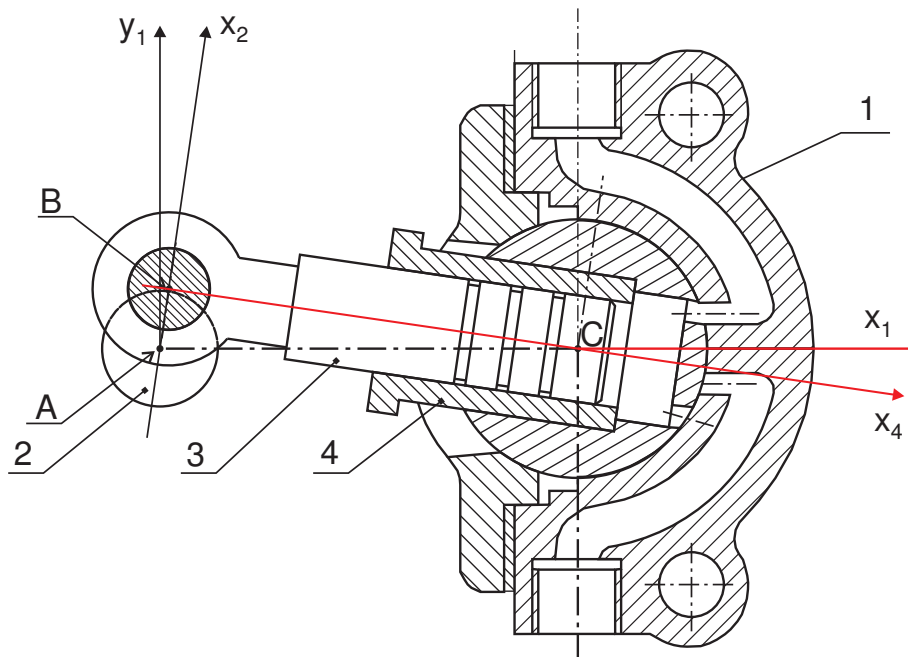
Dessin d'ensemble de la pompe oscillante
